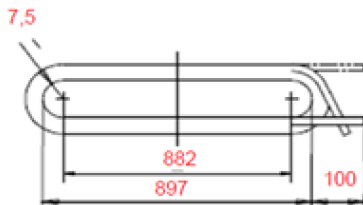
Recorte do plano de bobinagem- Dimensões da navete (em mm)
